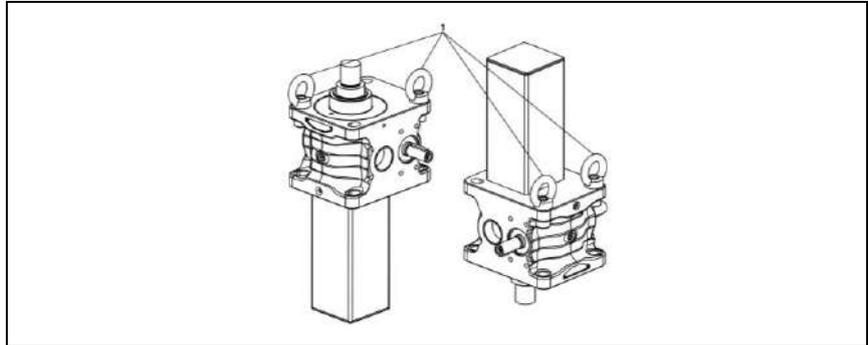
Ringschrauben (1) oder Ringmuttern (nicht im Lieferumfang)
